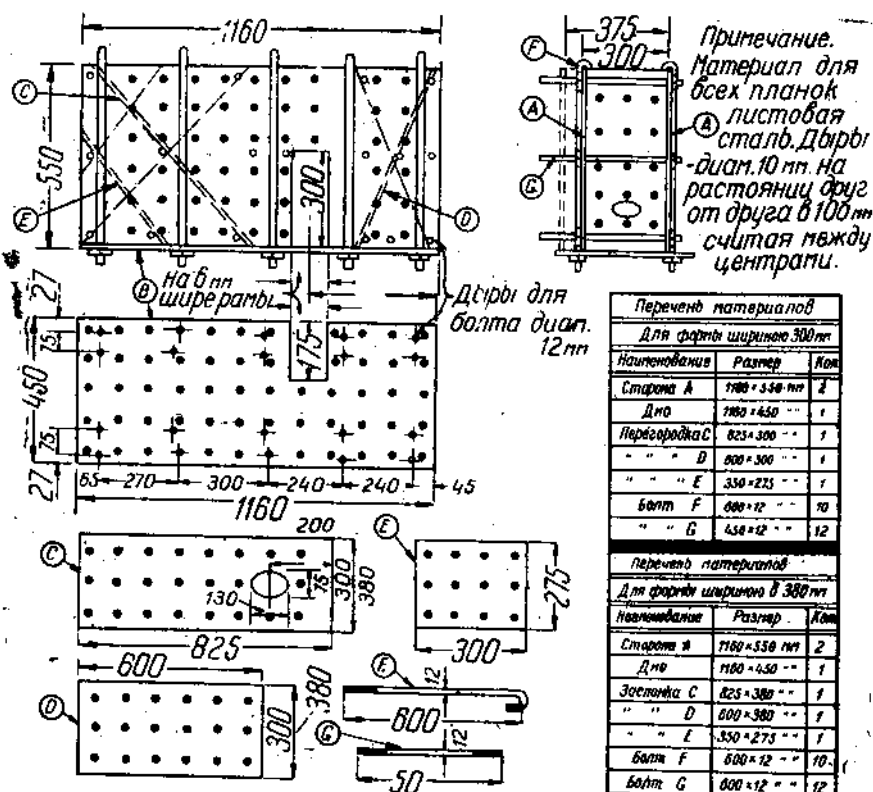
Детали стандартной сварочной формы для термитной сварки частей паровых рам с сечением до 160 × 200 мм.
